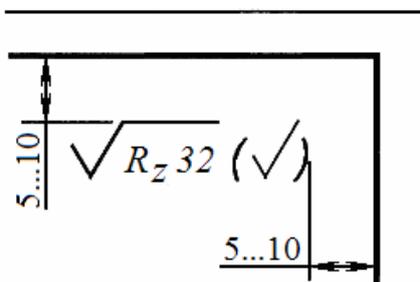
Обозначение поверхностей с одинаковой шероховатостью
